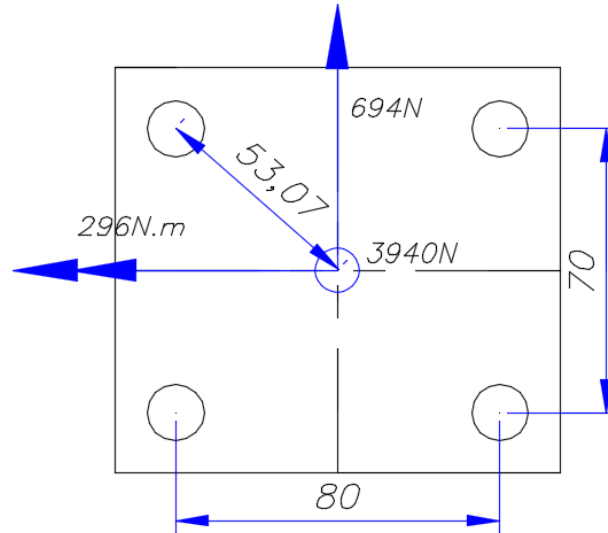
Dimensiones de unión atornillada de reductor para tornillos M12.
